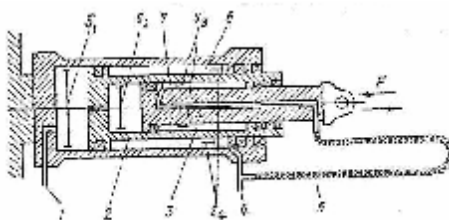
Схема телескопического гидроцилиндра:
